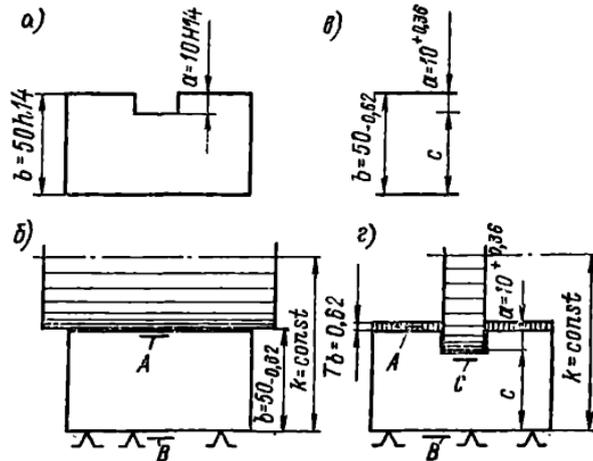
Фрезерование паза от опорной технологической базы B , не совпадающей с конструкторской
